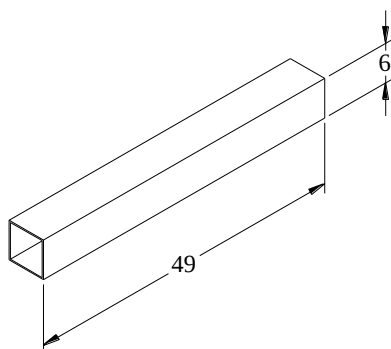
Dimensiones propuestas para las vigas. Fuente. Propia.
